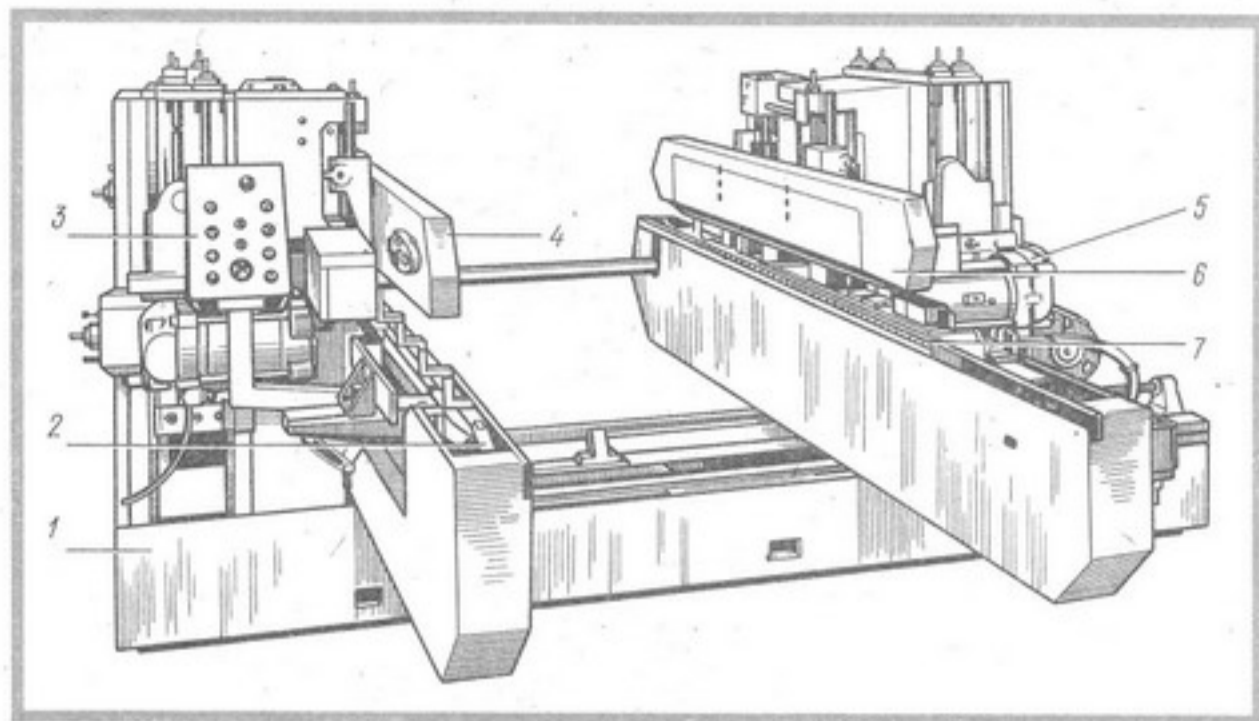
Двусторонний шипорезный рамный станок ШД10-8:
